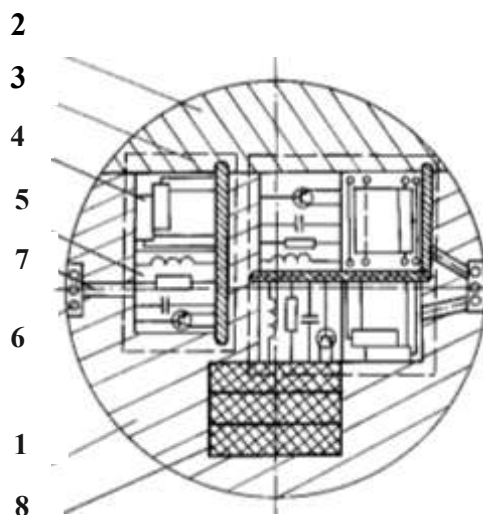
Трёхкомпонентный радиоакселерометр: 1 – корпус; 2 – крышка;
